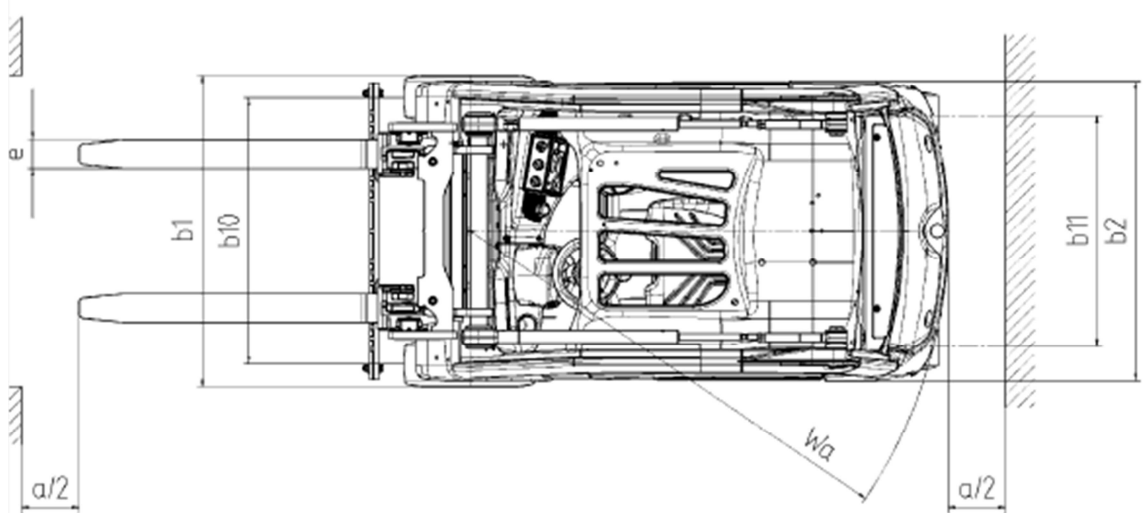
Planta máquina elevadora. Fuente: catálogo Linde
